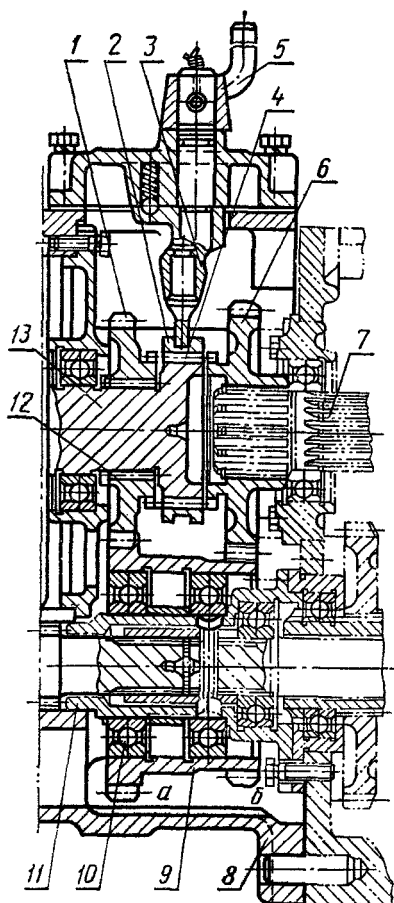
Понижающий редуктор (делитель) коробки передач тракторов МТЗ-80 и МТЗ-82:
